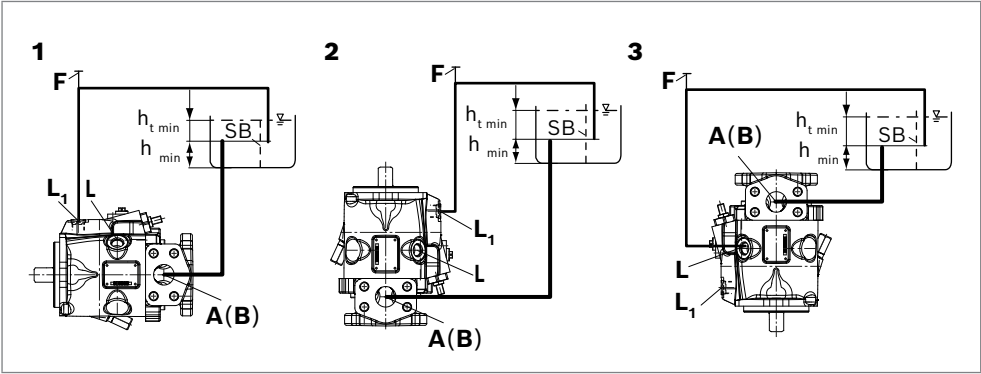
Untertankeinbau A10VZG mit Einbaulage 1–3
